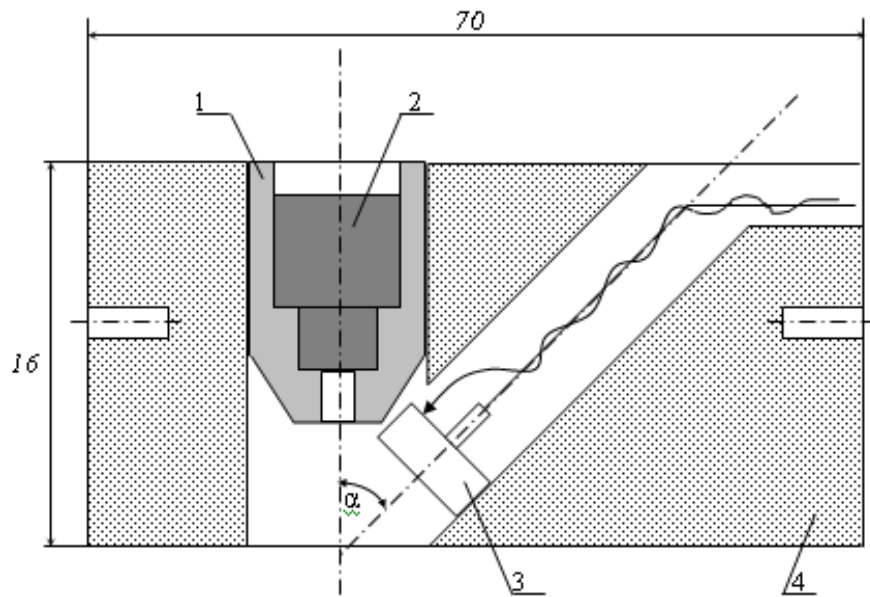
Конструкция первичного преобразователя для измерения толщины оболочек твэла промышленного реактора
